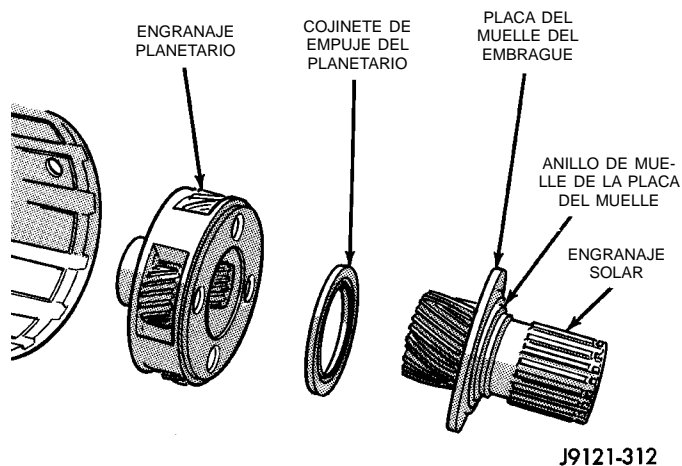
Desmontaje del engranaje solar, el cojinete de empuje y el engranaje planetario
